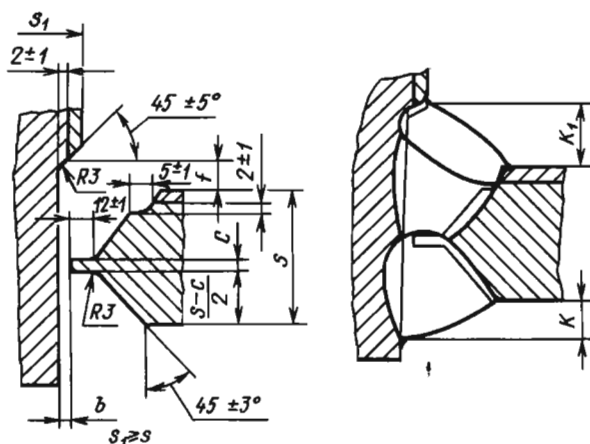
Разделка кромок и сварное тавровое соединение двухслойной стали (Т5)
